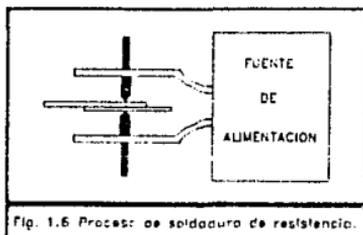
Proceso de soldadura de resistencia.
